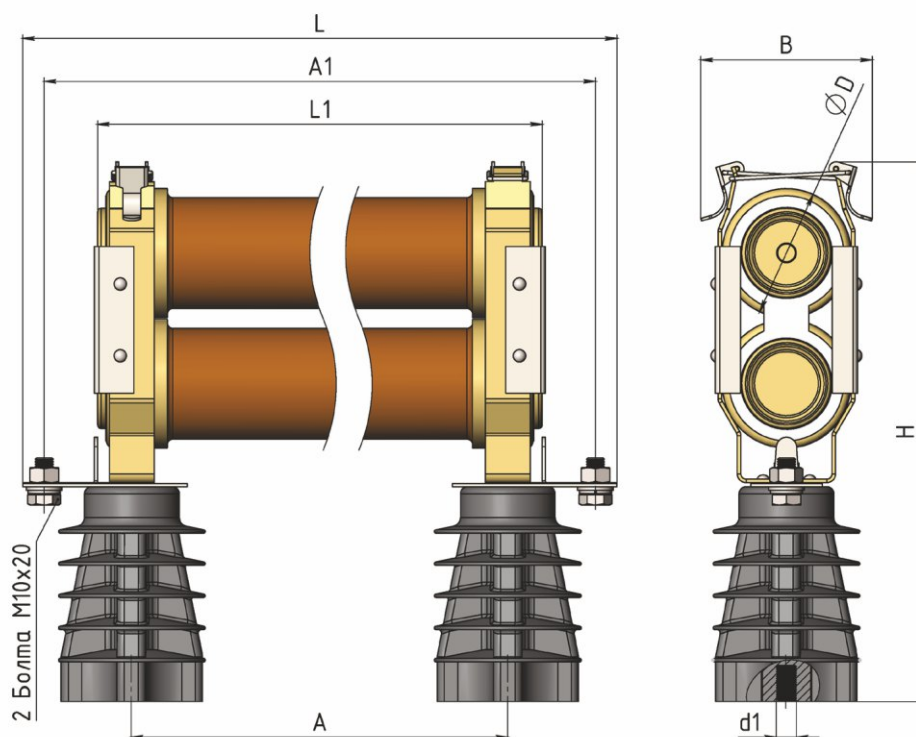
Внешний вид и основные размеры предохранителя ПКЭ класса напряжения 35кВ
